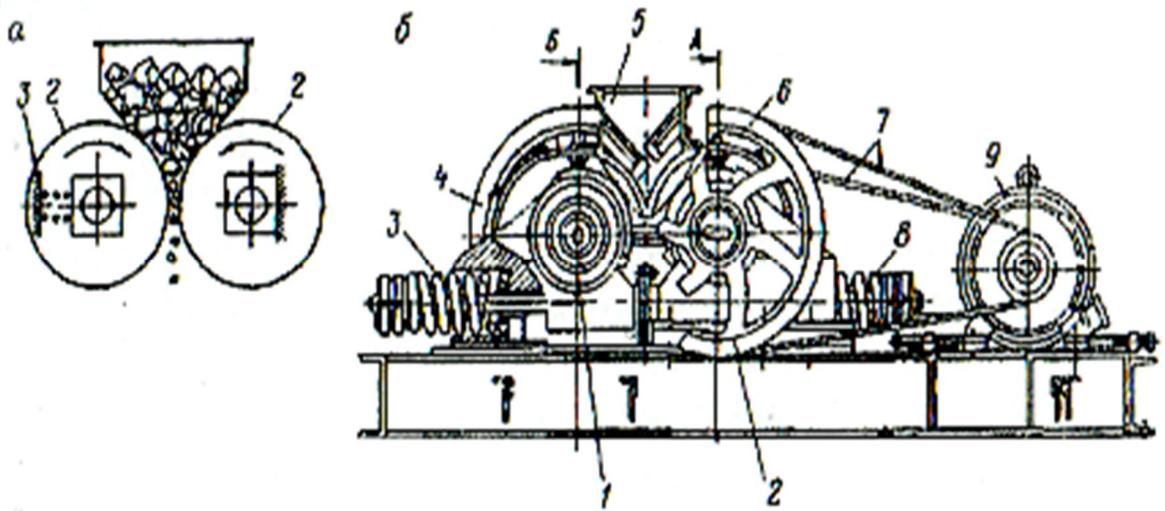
Принцип действия (а) и общий вид (б) двухвалковой дробилки типа ДВГ-2М:
